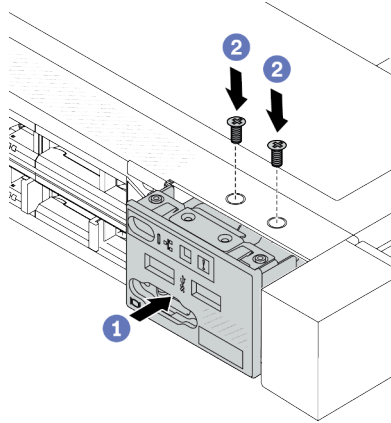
Instalar um módulo de E/S frontal no chassi de 2,5 pol.
